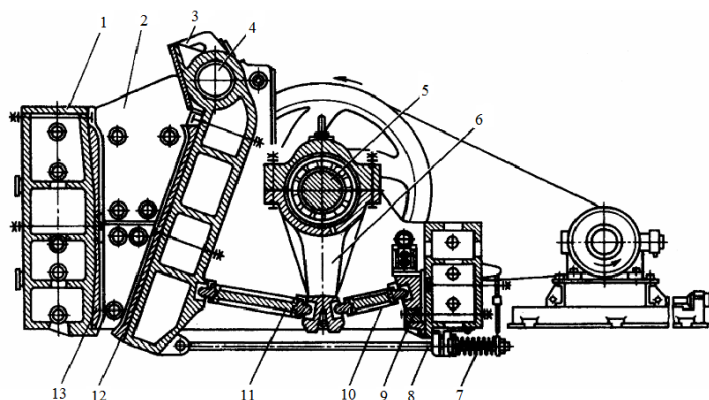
Конструкция щековой дробилки с простым движением щеки:
